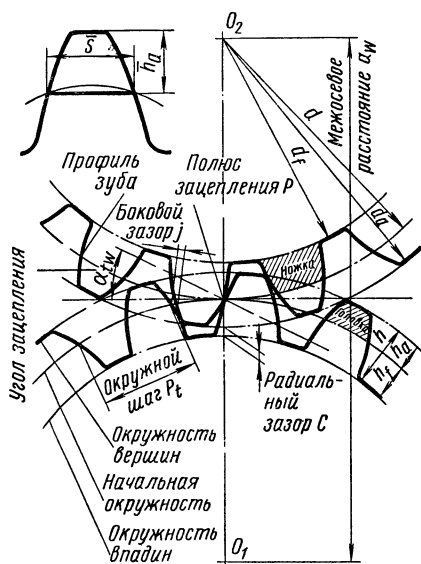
Схема зацепления в передачах цилиндрическими зубчатыми колесами
